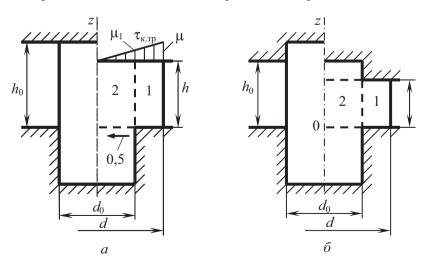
Схемы высадки фланца (a) и высадки поперечного утолщения (δ)
